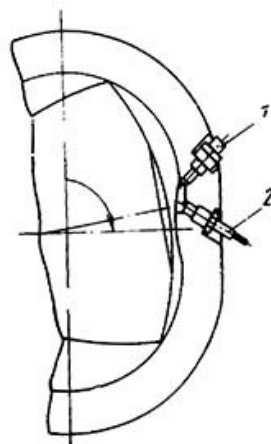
Схема расположения форсунки и свечи в многотопливном РПД фирмы Кертис-Райт:
